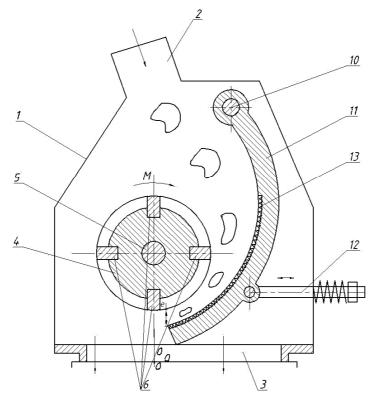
Поперечный разрез роторной дробилки *I* - корпус, 2 – загрузочный патрубок; *3* – разгрузочный патрубок; *4* – ротор; *5* – вал; *6* – била; *7*, *8* –стороны била; *10* – ось; *11* – отражательная плита; *12* – подпружиненная тяга; *13* – клиновые режущие выступы
